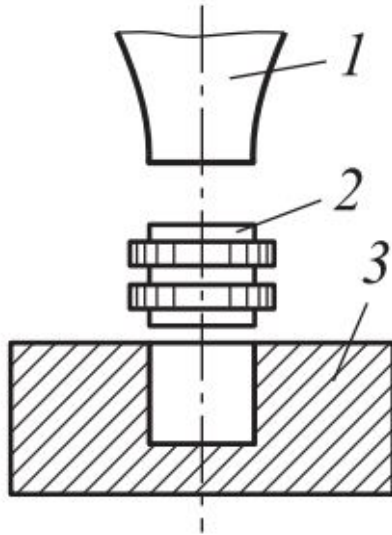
Схема запрессовки металлической детали в пластиковую:
